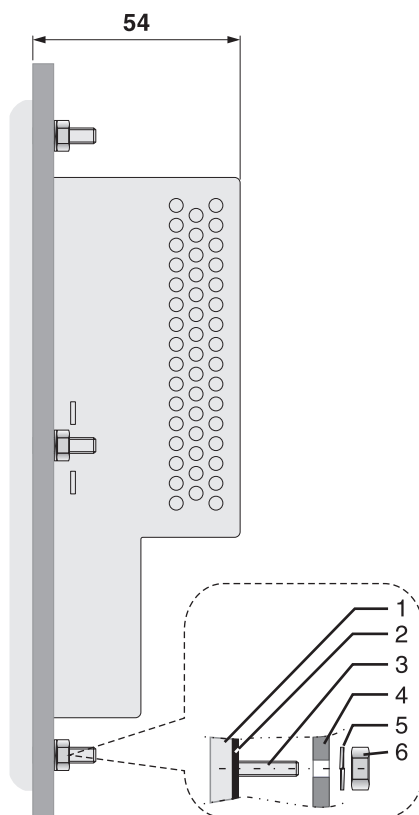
Seitenansicht, Einbautiefe (Maße in mm)
